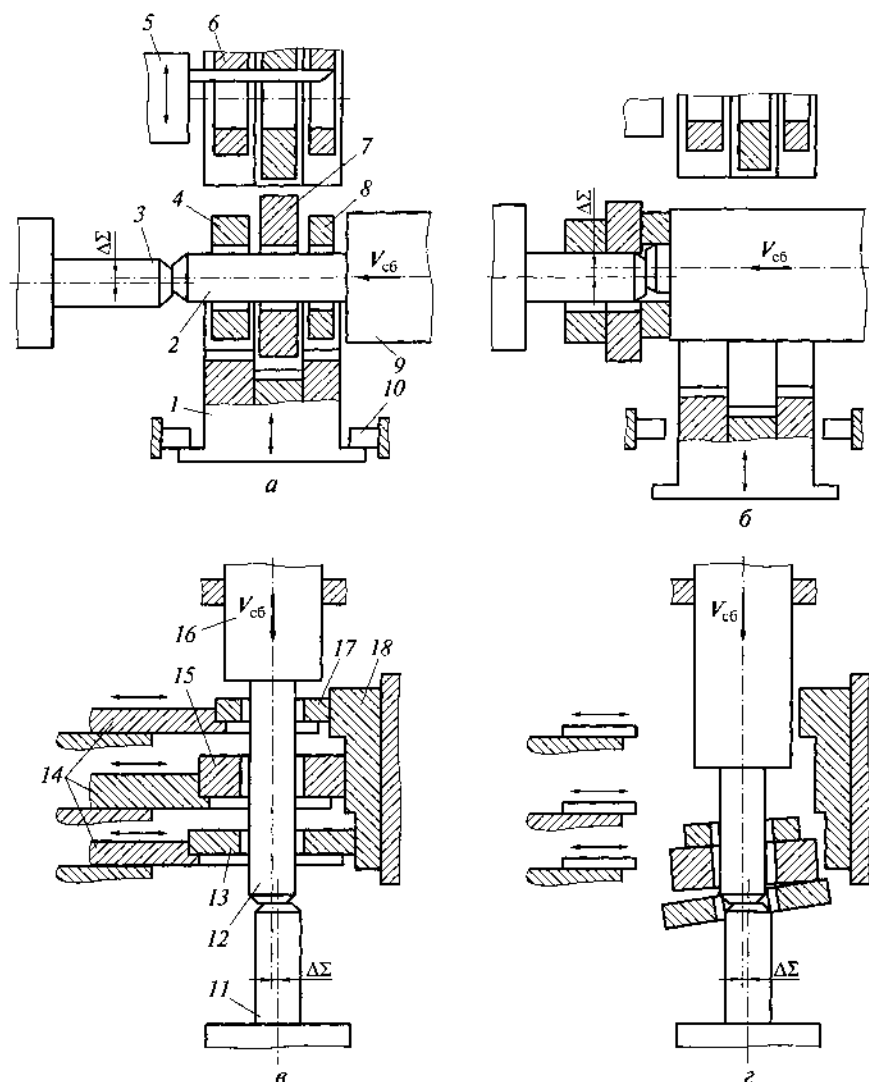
Схемы сборочных механизмов (*а...г*) для одновременной сборки группы деталей:
